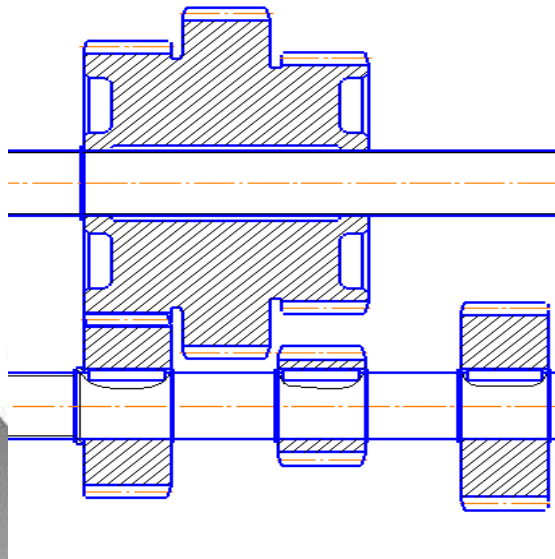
Конструктивна схема переміщення та положення блока зубчастих коліс Б2– зачеплення Z25/Z55
